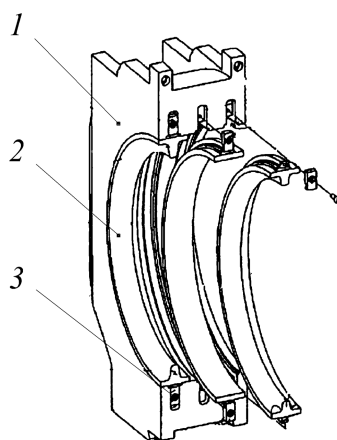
Півформа гофратора: 1 – обойма; 2 – формувальний вкладиш; 3 – гвинт
